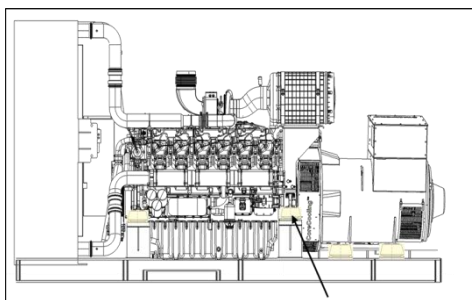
Г Проверка креплений/опор силовой установки (двигатель и генератор показаны условно)
